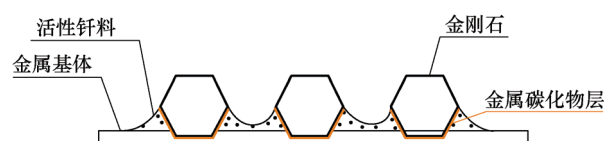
金刚石颗粒活性金属钎焊结构示意图
